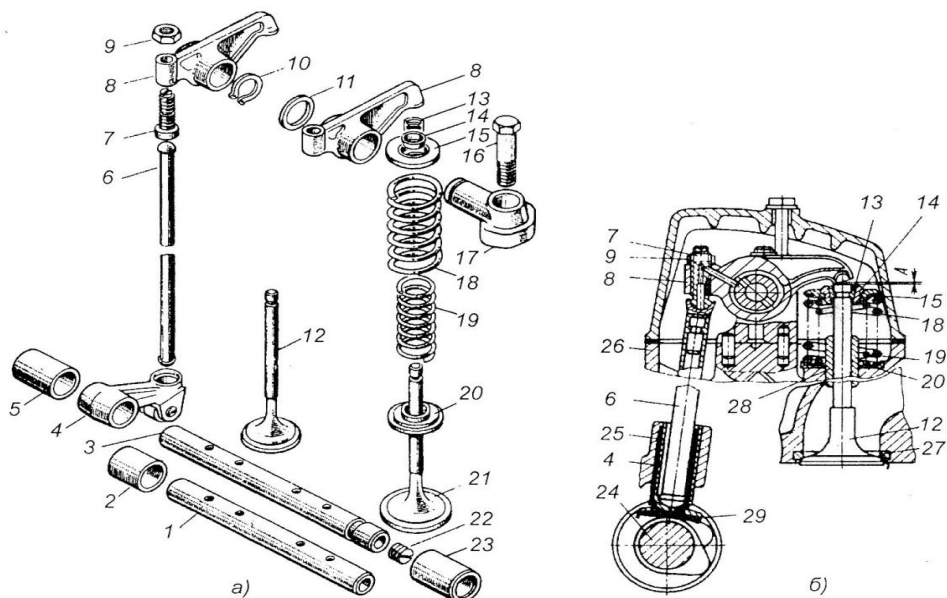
Детали (а) и механизм газораспределения (б): 1 – средняя ось толкателей; 2 – распорная втулка; 3 – крайняя ось толкателей; 4 – толкатель; 5 – промежуточная втулка; 6 – штанга; 7 – регулировочный винт; 8 – коромысло; 9 – контргайка; 10 – стопорное кольцо; 11 – упорная шайба; 12 – выпускной клапан; 13 – сухарь; 14 – втулка; 15 – тарелка пружины; 16 – болт; 17 – ось коромысла; 18 – внешняя пружина; 19 – внутренняя пружина; 20 – шайба; 21 – выпускной клапан; 22 – пробка; 23 – задняя втулка оси толкателей; 24 – распределительный вал; 25 – направляющая толкателя; 26 – головка блока цилиндров; 27 – седло клапана; 28 – направляющая втулка; 29 – наплавка на толкателе
